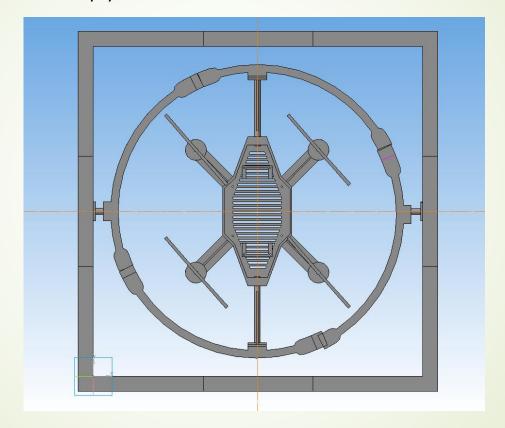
Сборка стенда САПР Компас-3D, вид сверху
